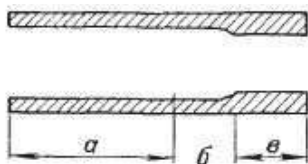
Разрез ствола со сверловкой чок, показывающий сущность этой сверловки:
